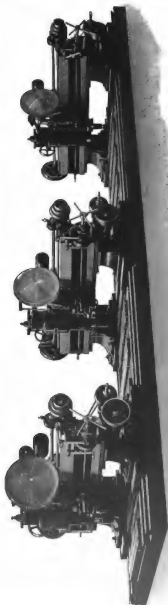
Vereinigte Rahmenstoß- und Fräsmaschine (Werkzeugmaschinenfabrik Collet &amp; Engelhard).
